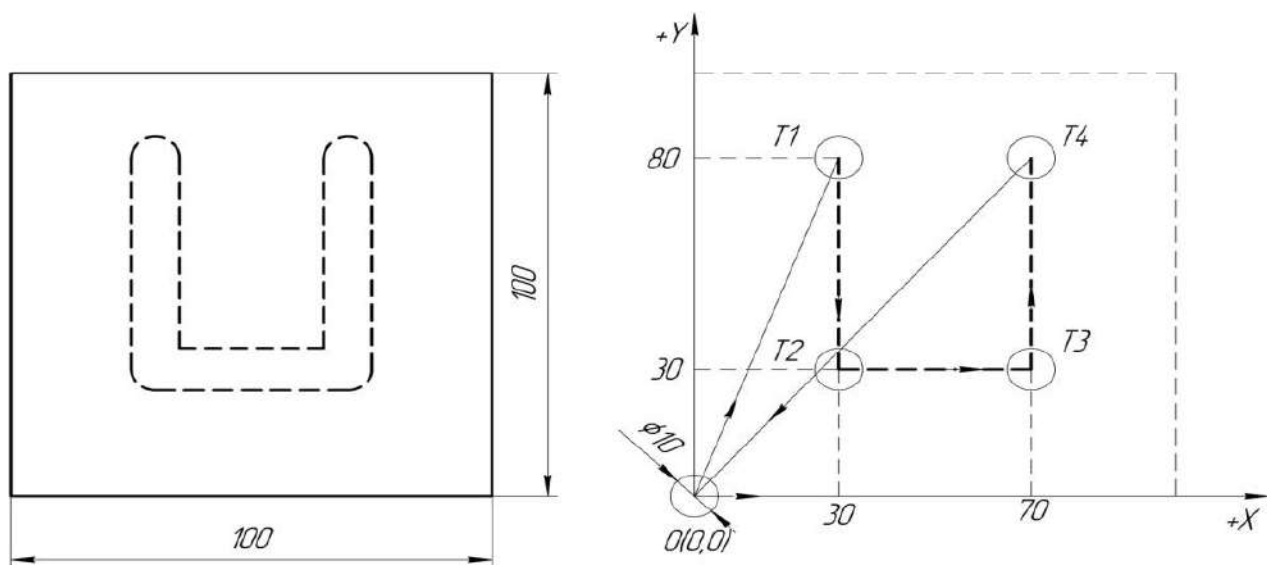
Ескіз заготовки та розташування її в прямокутній системі координат X\_Y
